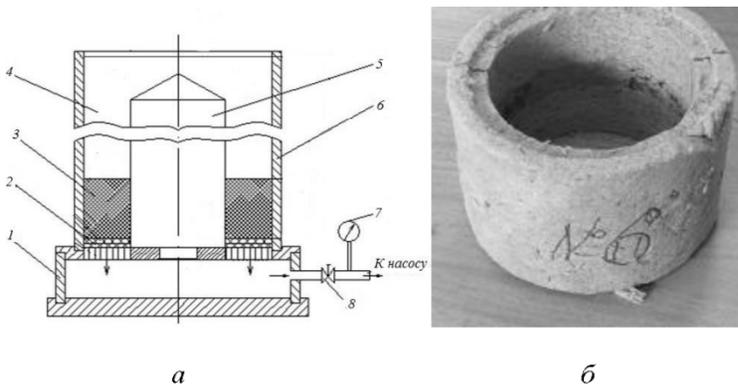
Схема фильтрационного осаждения волокон из пульпы (а) и цилиндрический образец ТИП на основе базальтового волокна и глинозема (б): 1 — камера; 2 — фильтровальная перегородка; 3 — слой осадка ТИМ; 4 — пульпа; 5 — оправка; 6 — корпус (труба); 7 — вакуумметр; 8 — запорный вентиль
